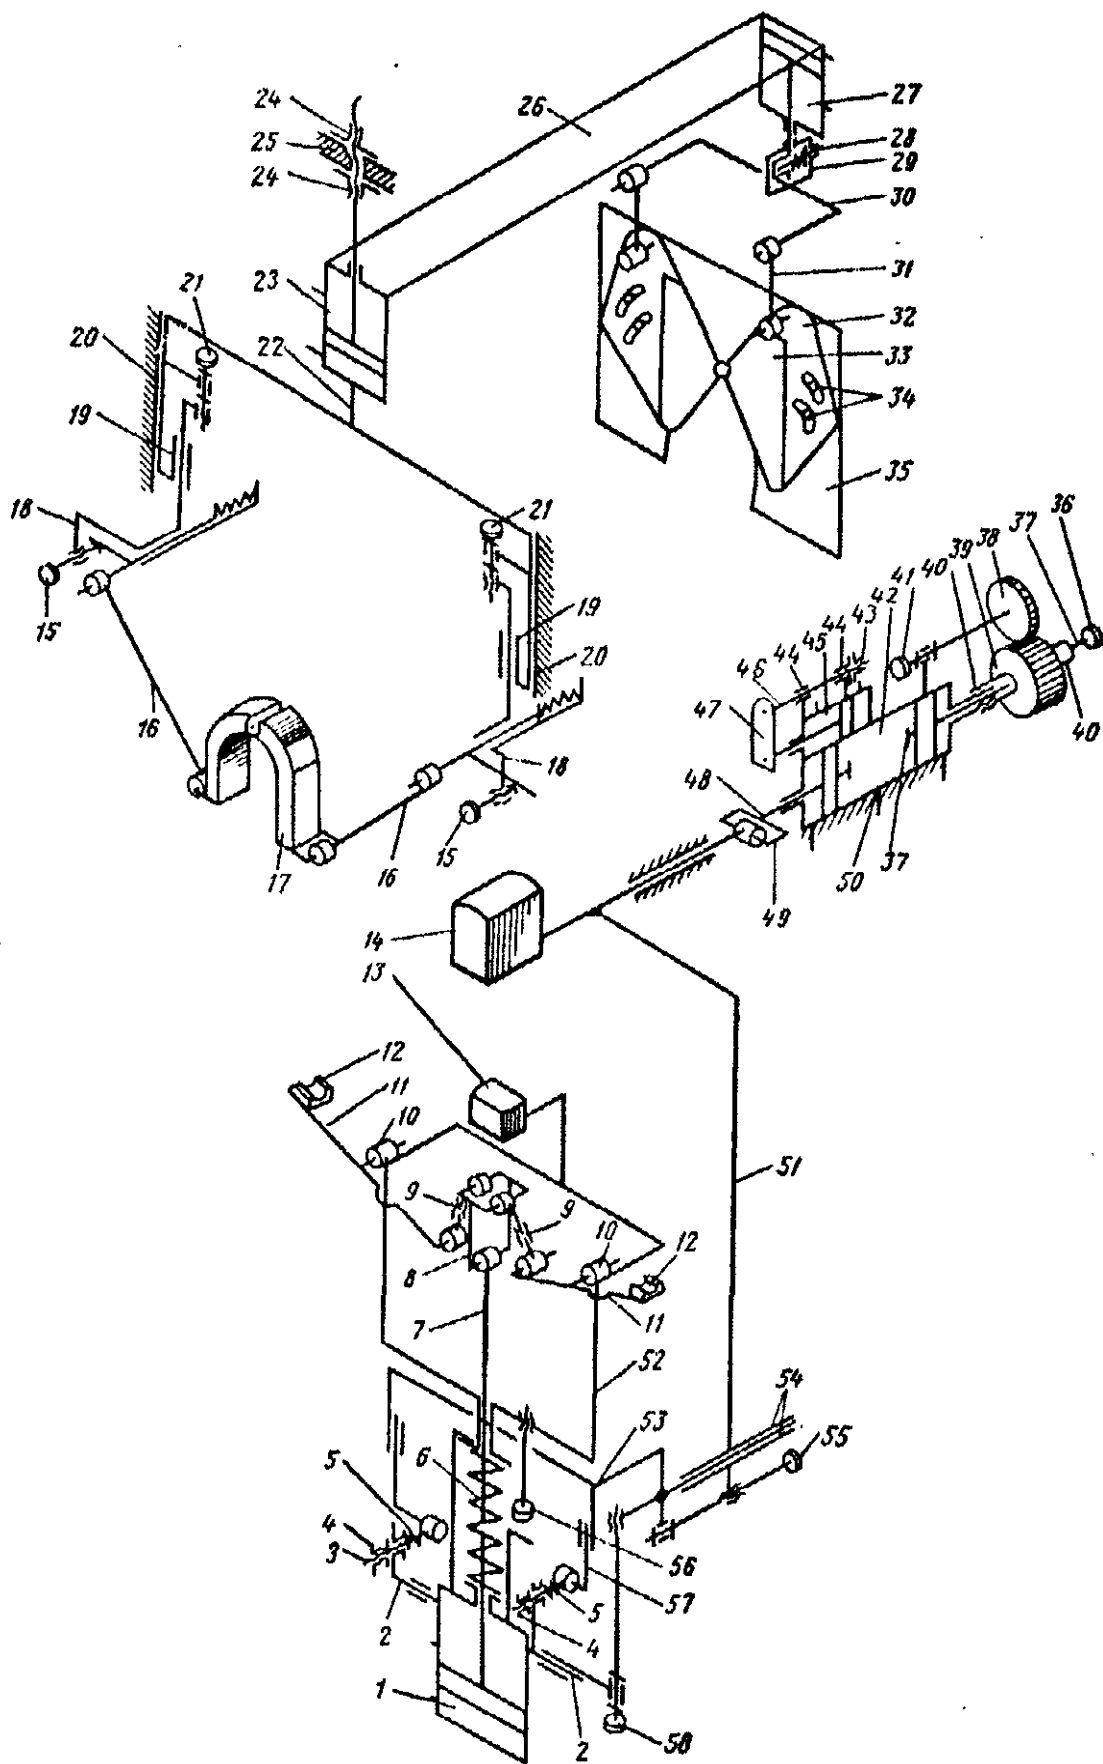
Кинематическая схема машины ЗФП-1-О
